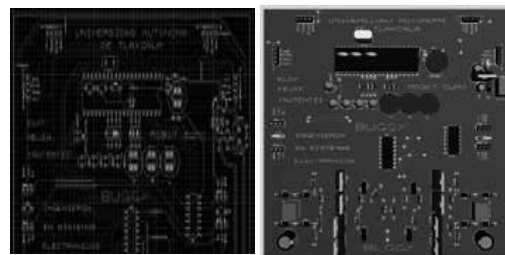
a y b. Diseño de las PCB en Ares de Proteus
